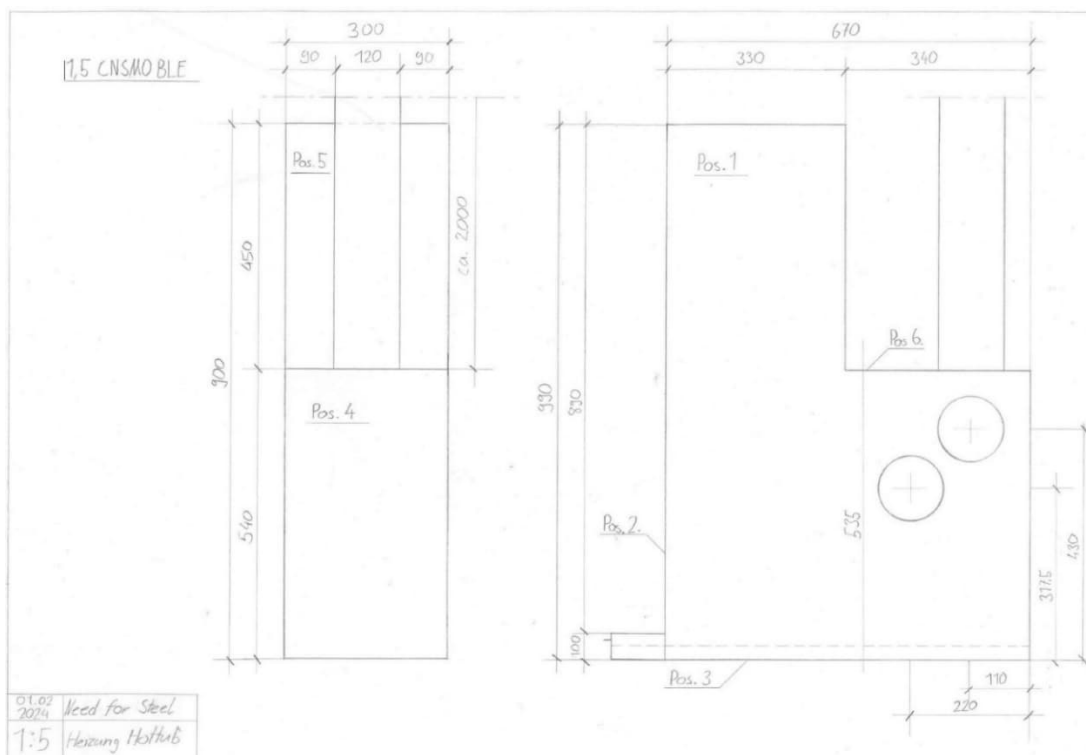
Plan mit Seitenrissen des Ofens (Originalplan siehe Anhang)
